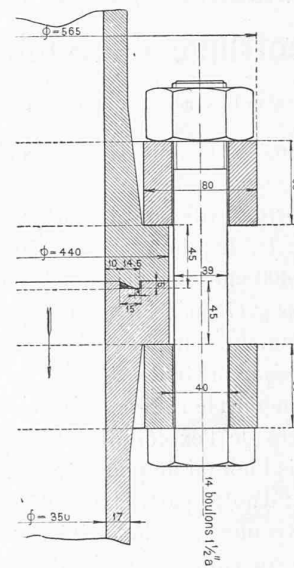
Assemblage des tuyaux soudés. — 1 : 5.
